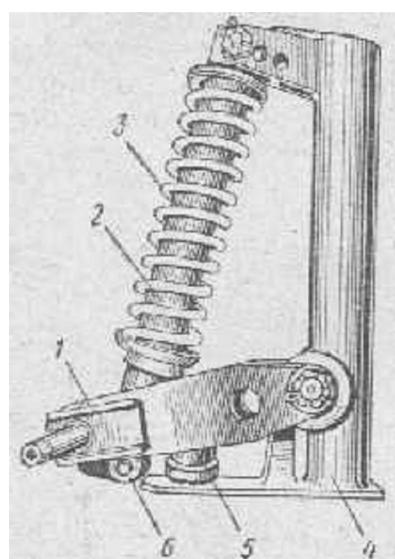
Узел подвески колеса прицепа новой конструкции (модель 560/01):
